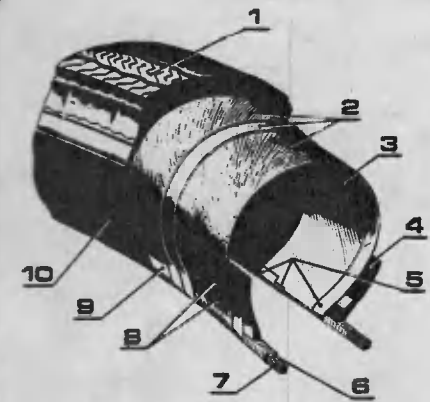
Конструкция шины с диагональным построением корда: 1 — рисунок протектора; 2, 5, 8 — слой каркаса; 3 — герметизирующий слой; 4 — наполнительный шнур; 6 — обертка бортового кольца; 7 — проволочное бортовое кольцо; 9 — чифер (крыльевая лента); 10 — резина боковины.
